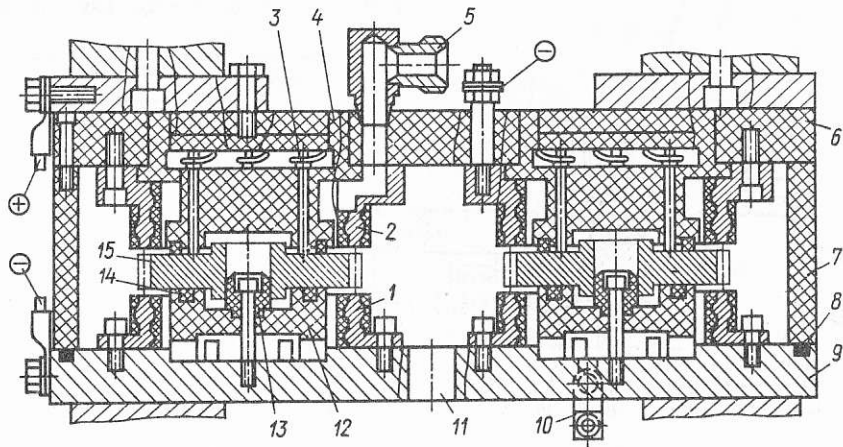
Приспособление для снятия заусенцев и притупления острых кромок на зубчатых колесах
